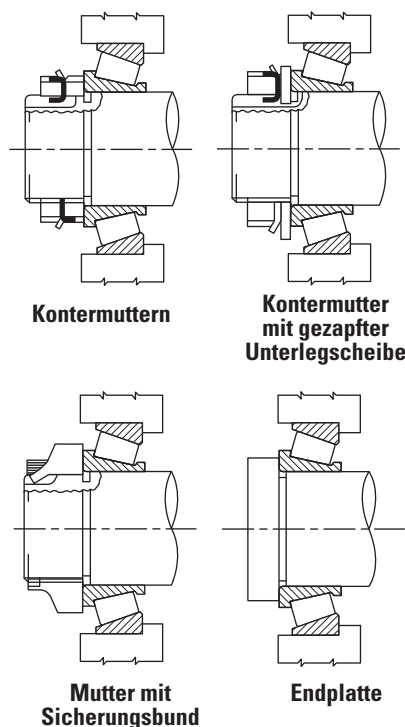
Vorrichtungen zur Lagereinstellung - indirekte Montage.
